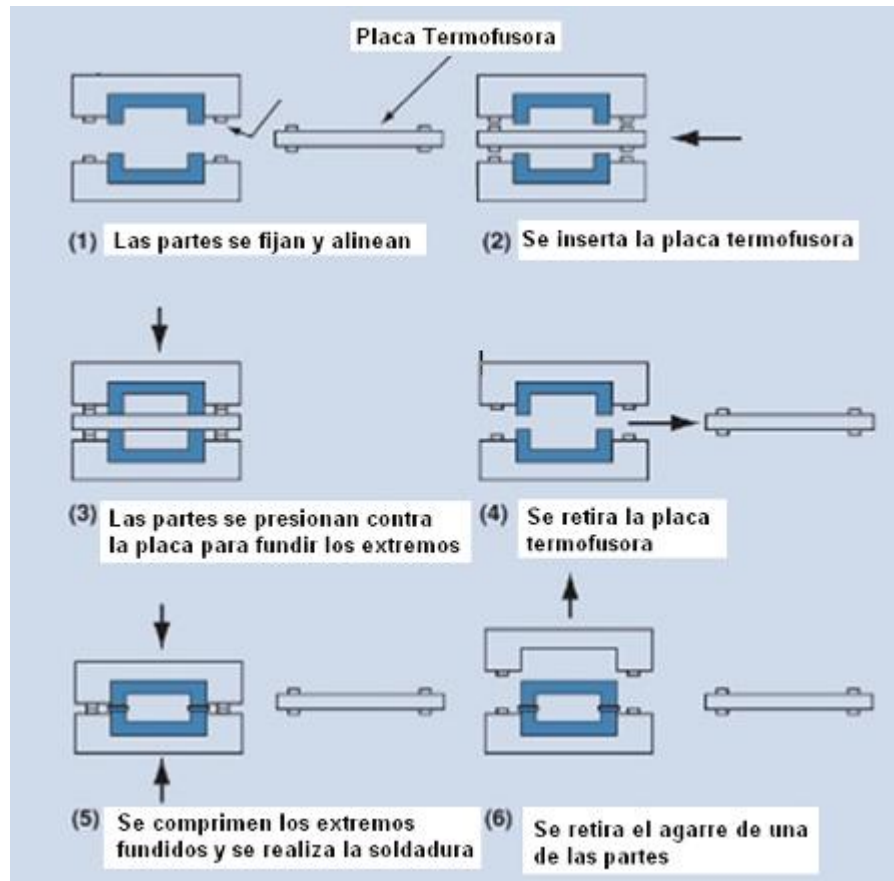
Esquema del proceso de soldadura por termofusión.
